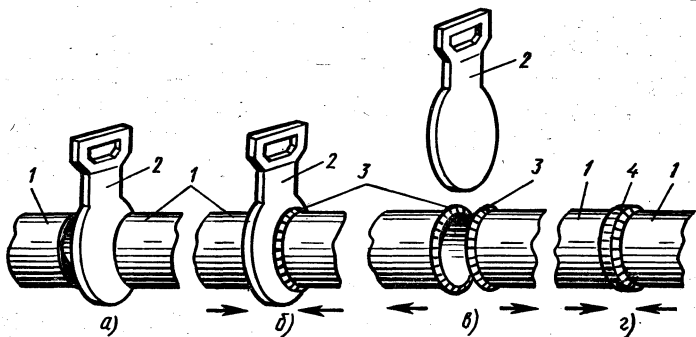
Технологическая последовательность соединения пластмассовых труб контактной стыковой сваркой:
